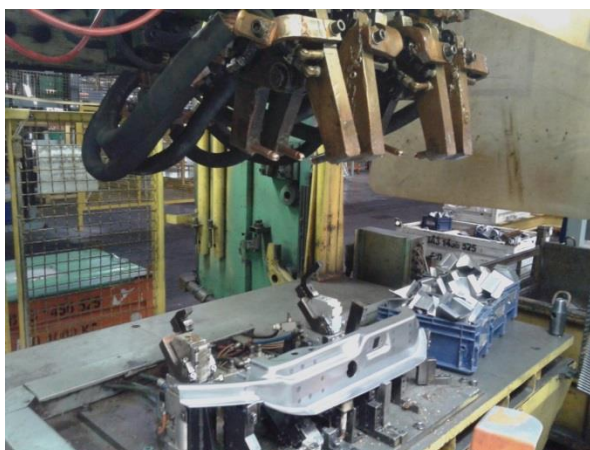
Сварочная оснастка многоэлектродной сварочной машины МСМ 503.618.421
